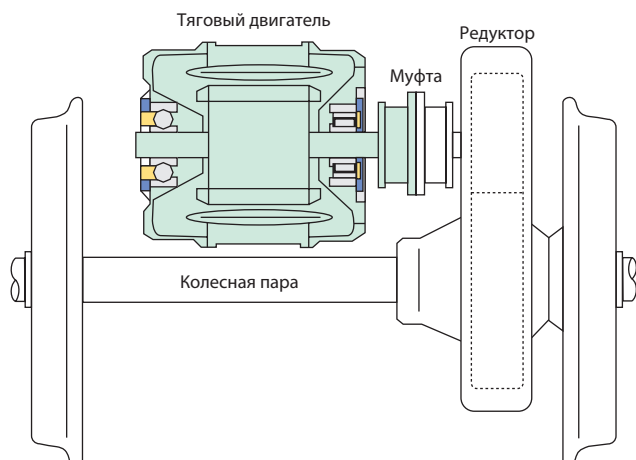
Колесно-моторный блок с асинхронным тяговым двигателем
